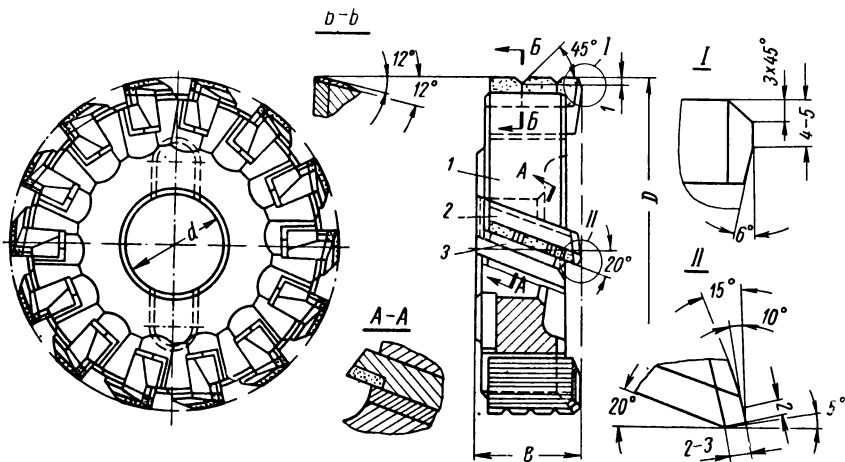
Торцово-цилиндрическая фреза со вставными твердосплавными ножами диаметром от 125 до 200 мм:
